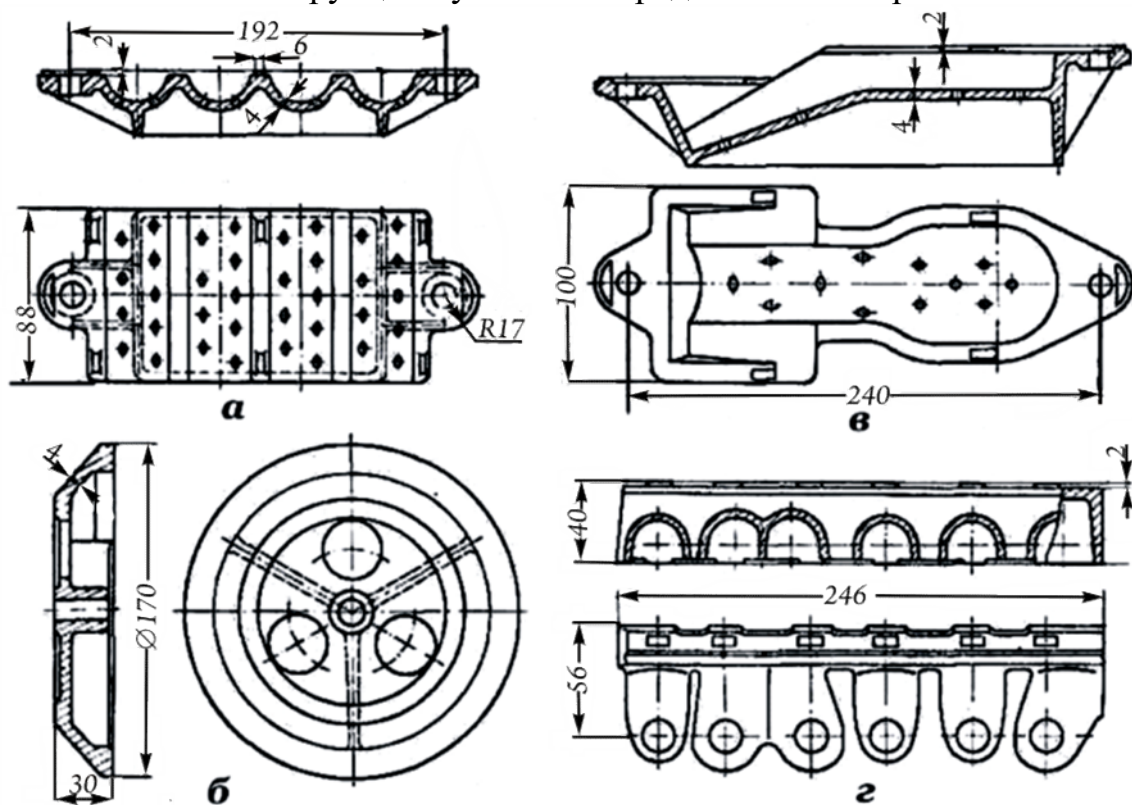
Типовые конструкции сушителей: а – сушитель для сушки круглых стержней; б – сушитель-вставка в стержень; в – сушитель для сушки стержней с фасонным разъемом; г – сушитель – боковая вставка в стержень
